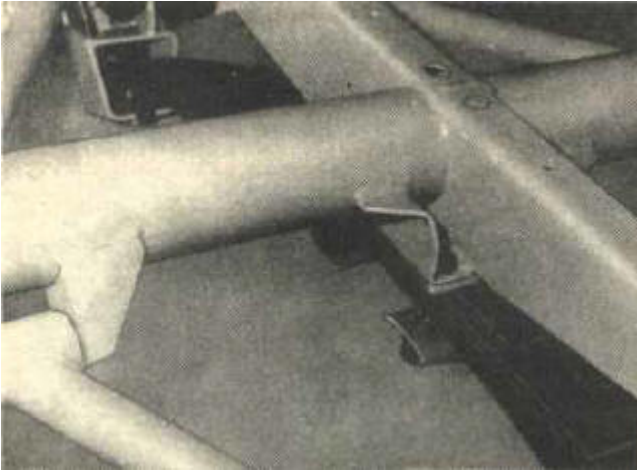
Befestigung der Blattfeder am Zentralrohrrahmen
